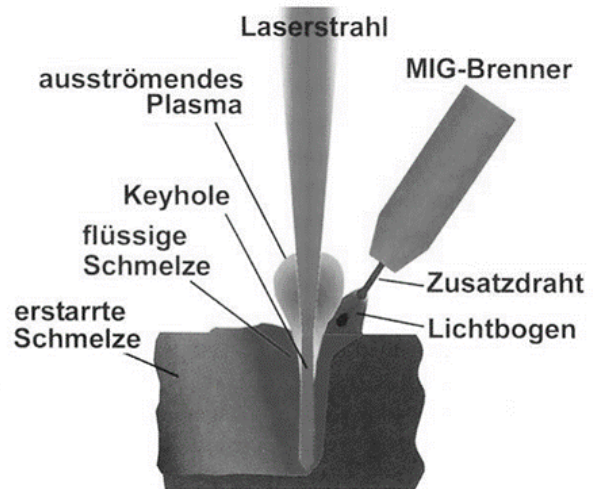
Schema des Laser-MSG-Hybrid-Schweißens
